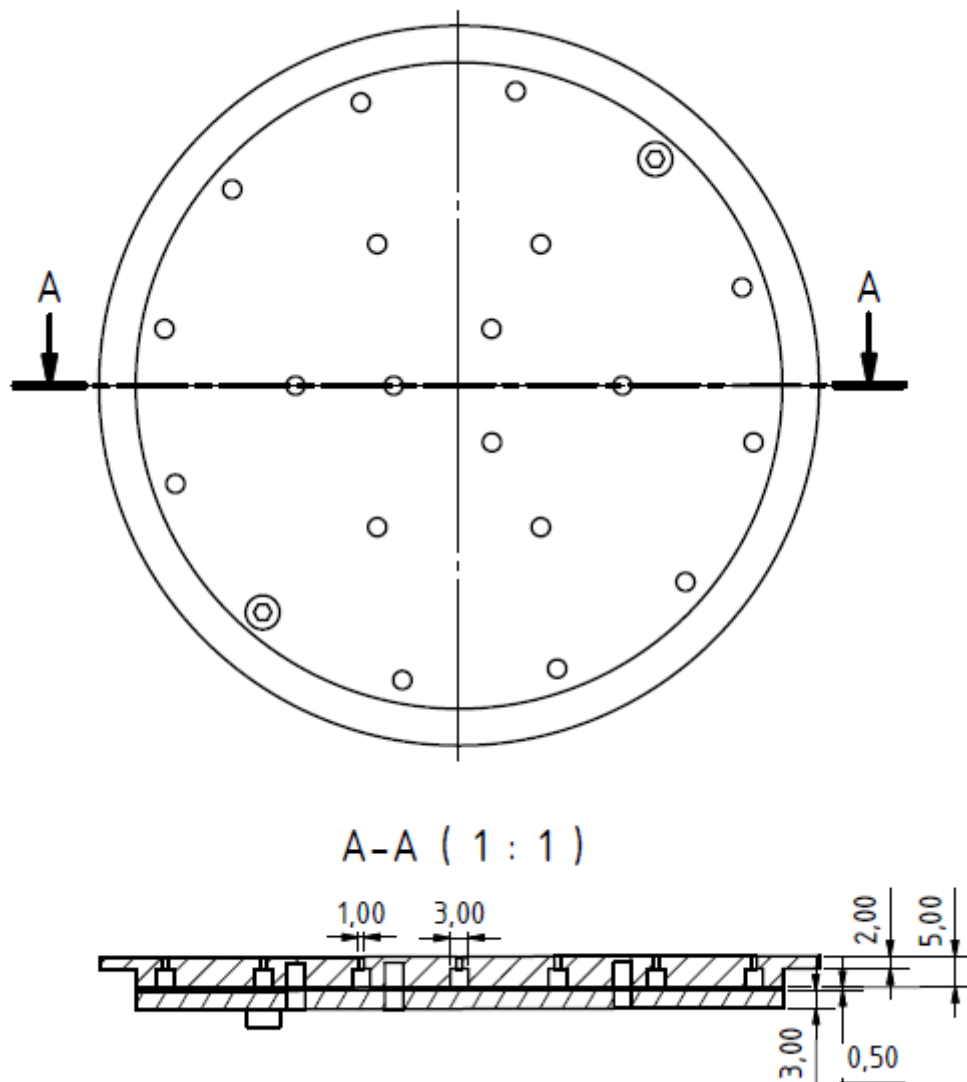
Technische Zeichnung des chemisch beständigen Gasverteilers
